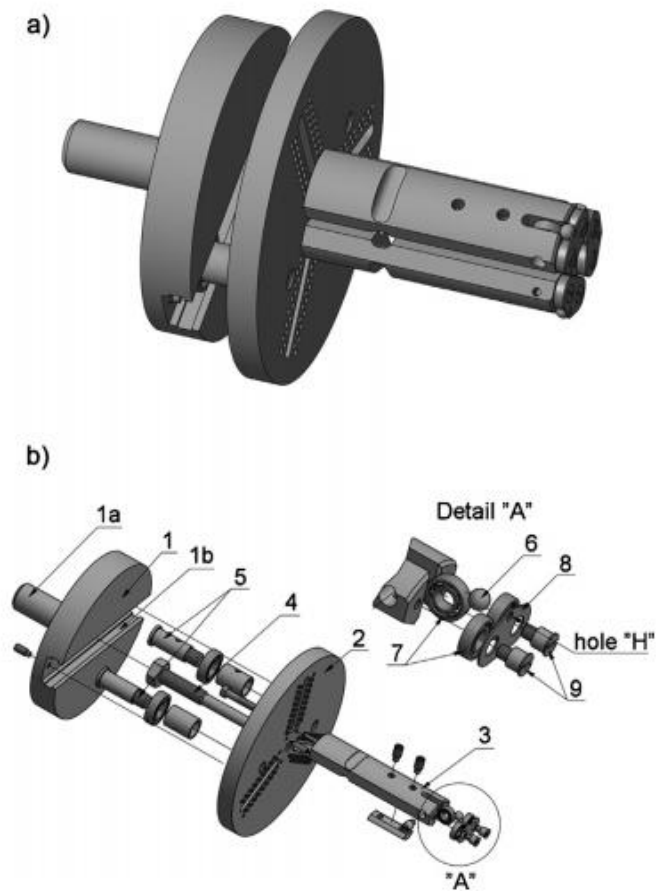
Конструкція спеціального інструменту для розкочування поверхні отвору [23]
